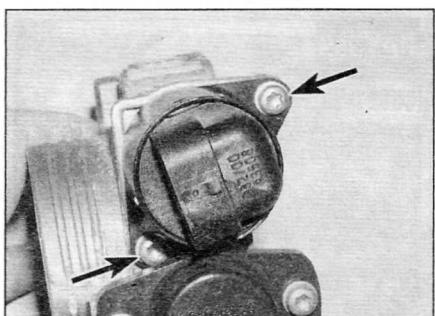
Затем выверните винты (отмечены стрелками) и снимите электродвигатель с корпуса дроссельной заслонки (модели с двигателем 1.4 л)
